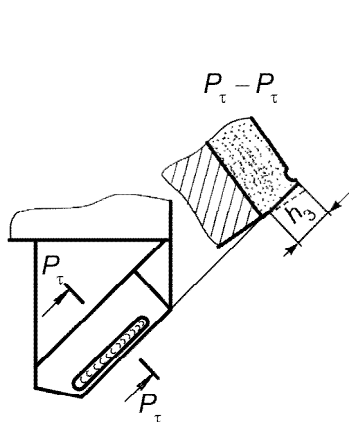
Схема износа ножа торцевой твердосплавной фрезы
